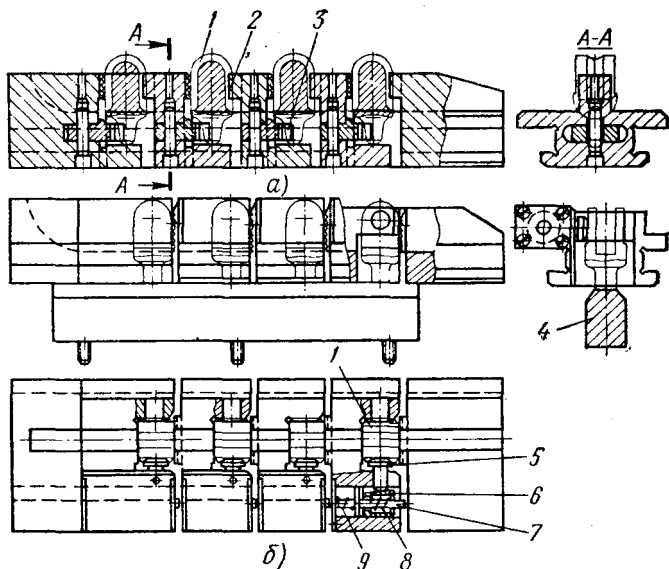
Наладка на универсально-наладочное приспособление для фрезерования:
